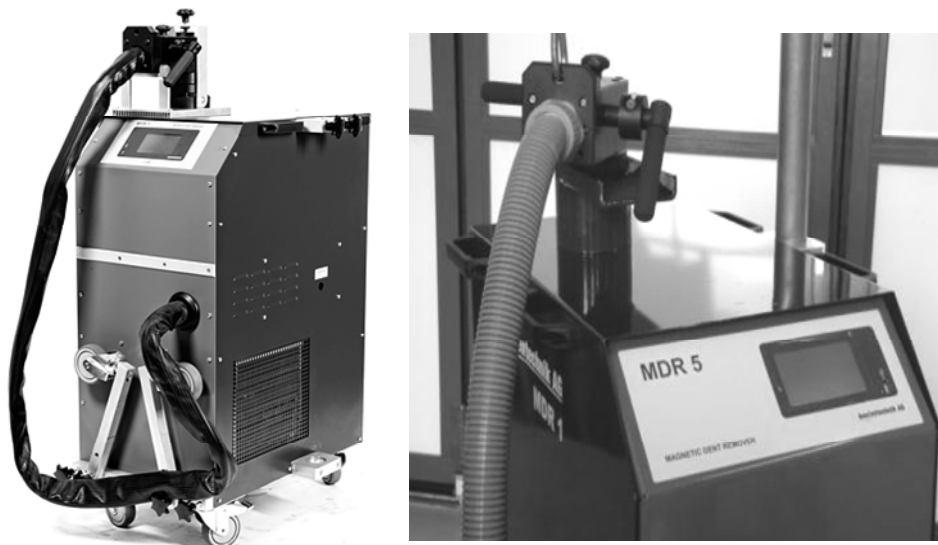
Загальний вигляд магнітно-імпульсної установки фірми "Тесла" (гнучкий кабельний зв'язок сполучає електричний вихід установки з інструментом)
